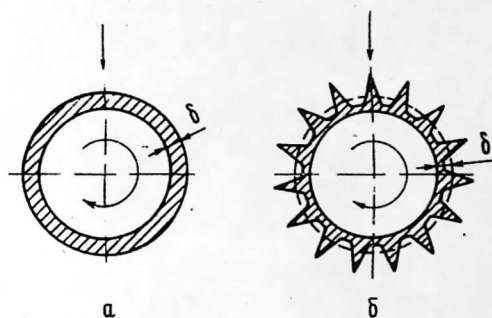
Схема оплавления сплошного металлического цилиндра электронным лучом, равномерно перемещающимся вдоль образующей цилиндра по линии, перпендикулярной плоскости чертежа:
